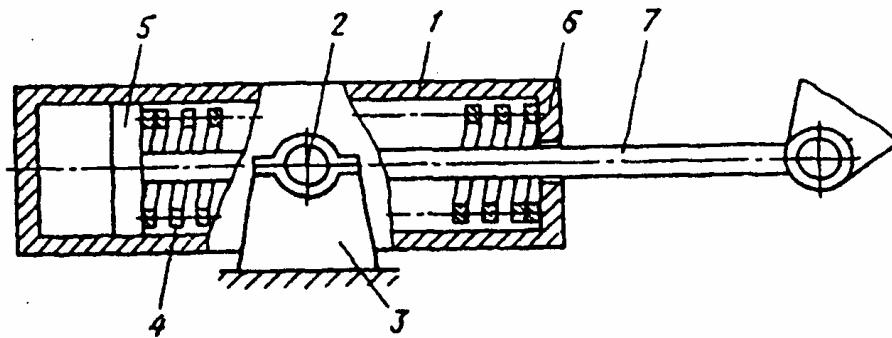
Пружинный уравновешивающий механизм тянувшего типа с качающейся колонкой
